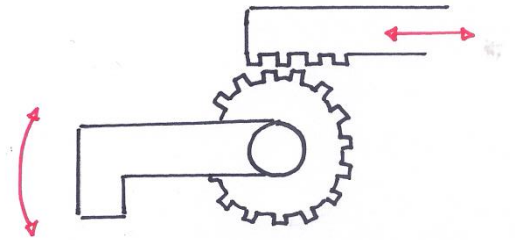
Croquis del mecanismo Engranaje-Cremallera.
